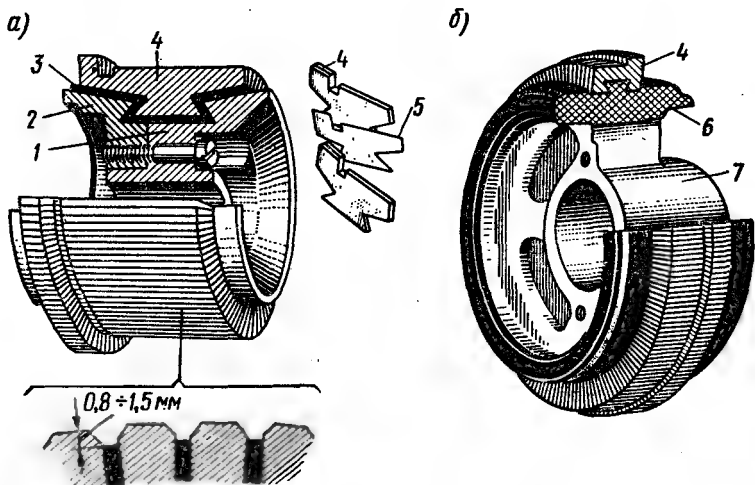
Устройство коллектора машины постоянного тока с металлическим и пластмассовым корпусом:
